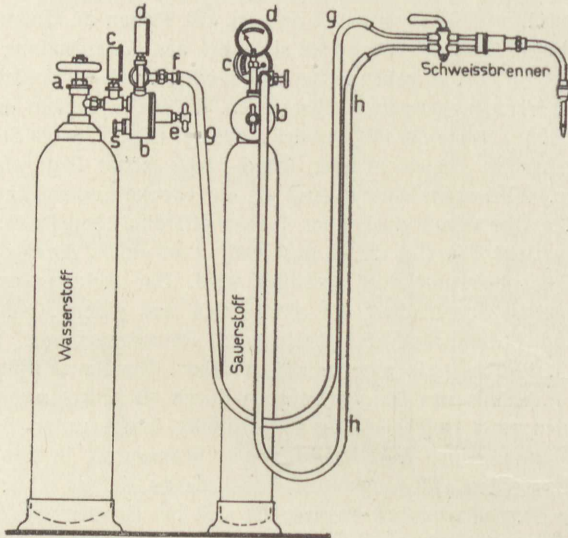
Wasserstoff-Sauerstoff-Schweißanlage.
